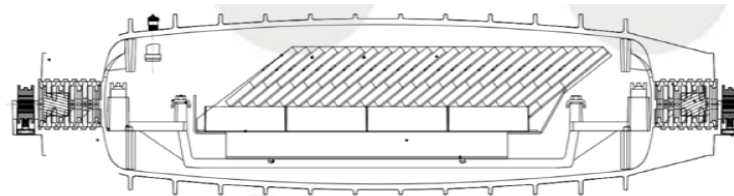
Vista interior. Detalle de la disposición de las 24 charolas y sistema hermético para proteger las
